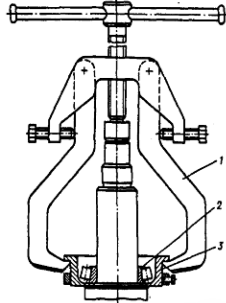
Захват для зняття внутрішнього кільця зовнішнього підшипника циліндричної шестерні середнього моста ПМ 1878-26-2: 1 – стискальні елементи; 2 – фіксатори; 3 – вал із різьбленням; 4 – ручка подачі.
